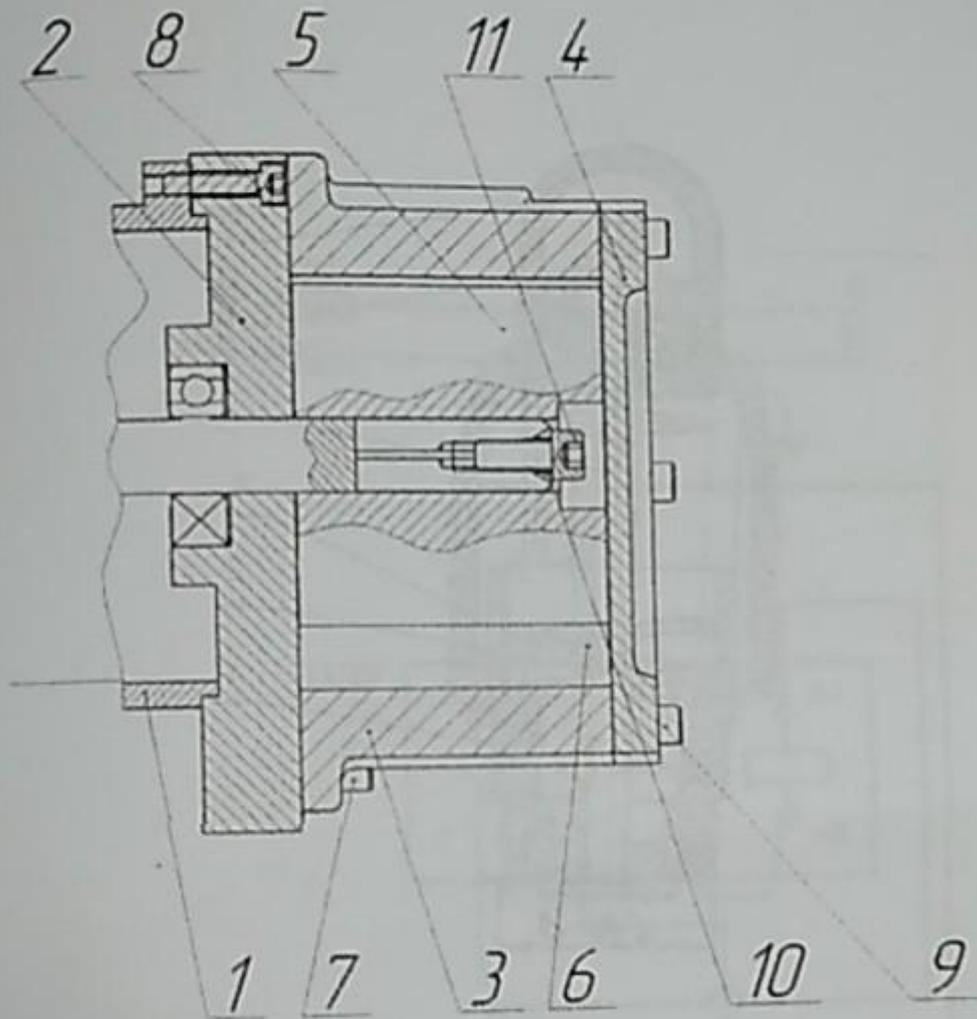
Вакуумный агрегат 1 - электродвигун; 2 - фланец; 3 - корпус; 4 - крышка; 5 - ротор; 6 - лопатка; 7 - гвинт M8x30 ; 8 - гвинт M6x30; 9 - втулка; 10 - гвинт M8x20.
